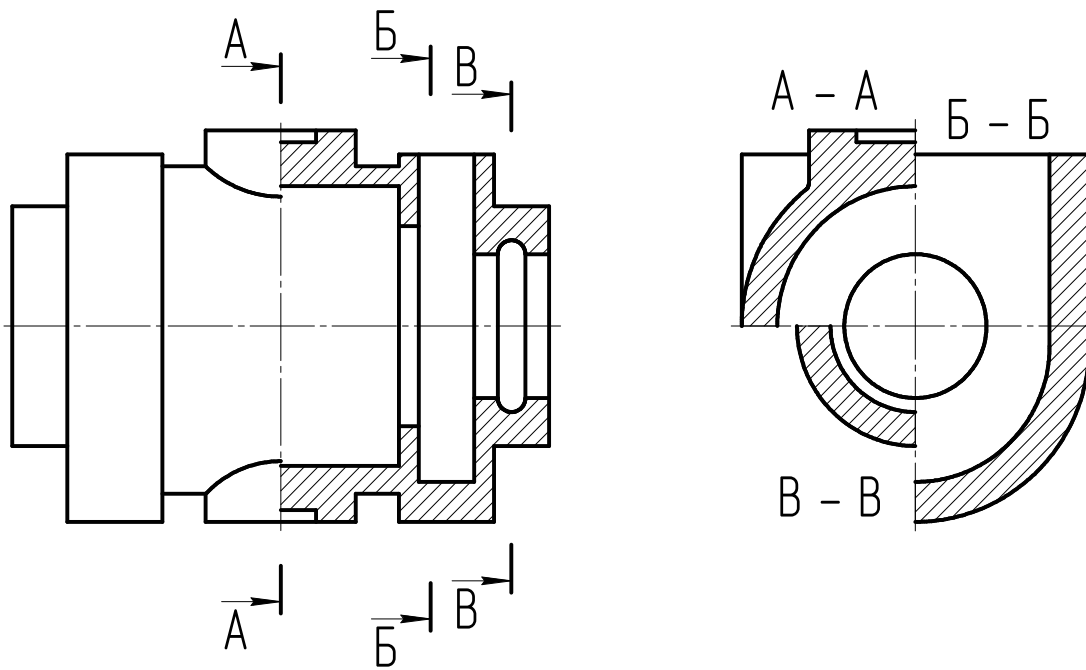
Поєднання чверті вигляду з частиною розрізу
